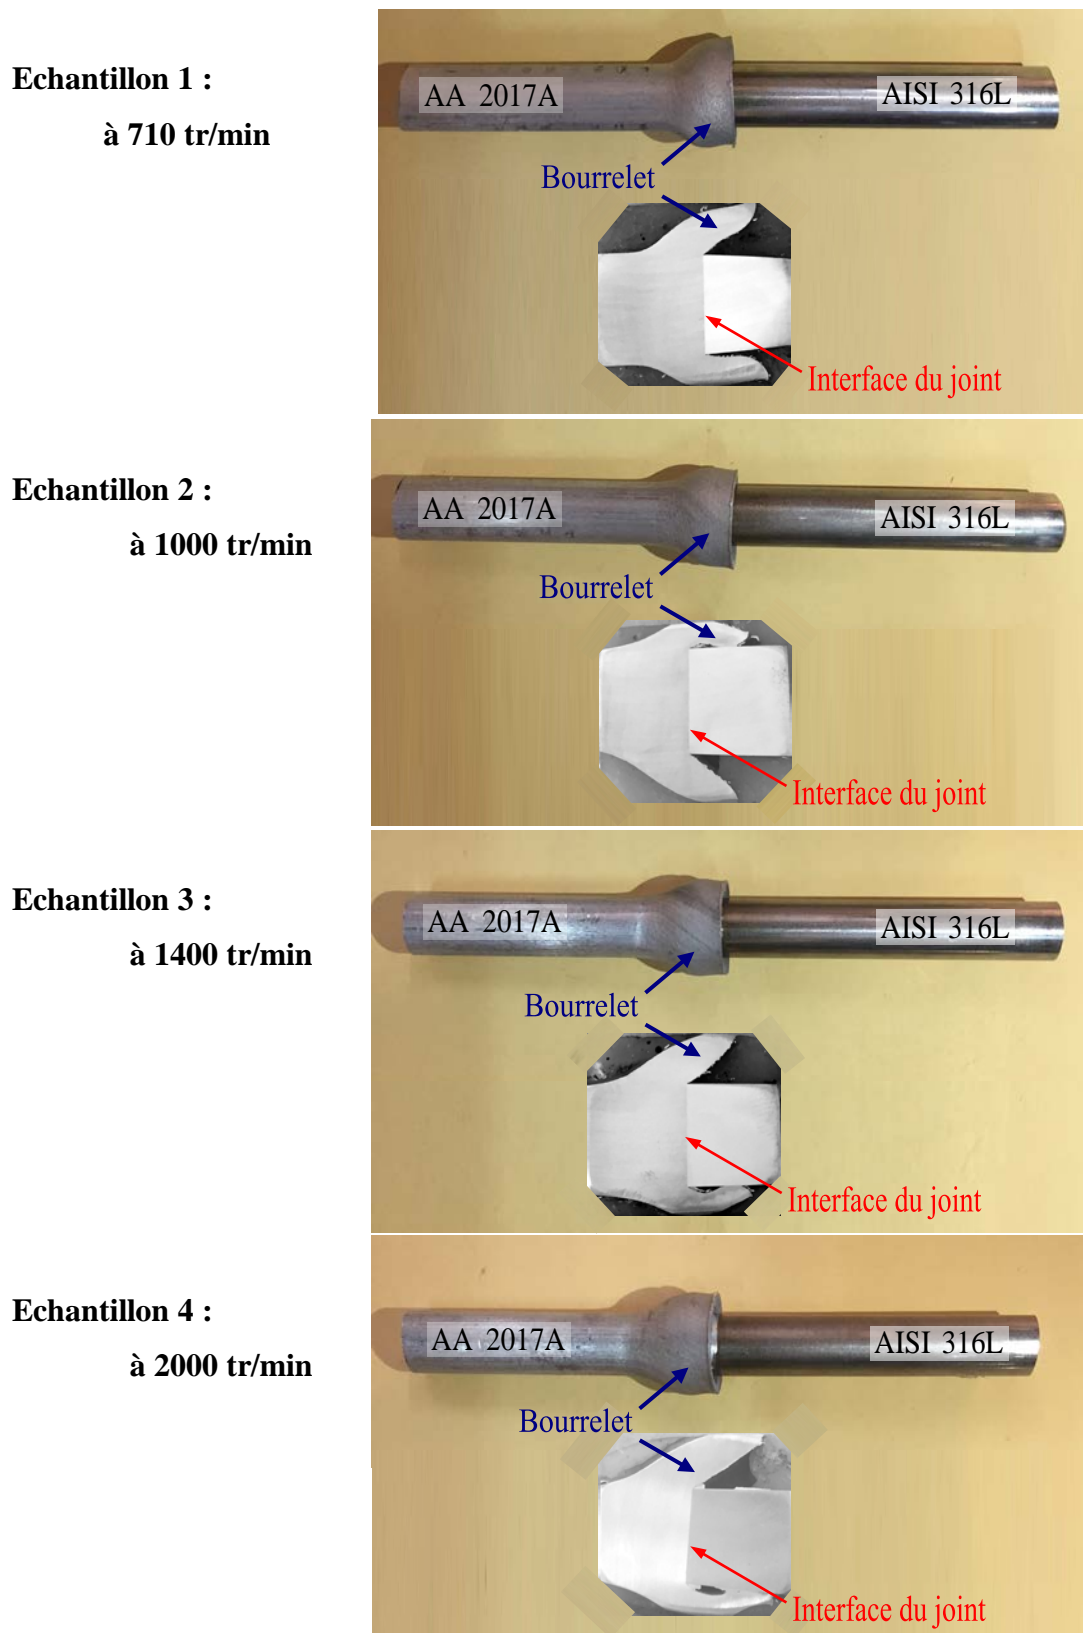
Joints dissimilaires acier inoxydable AISI 316L/alliage d'aluminium 2017A soudés
